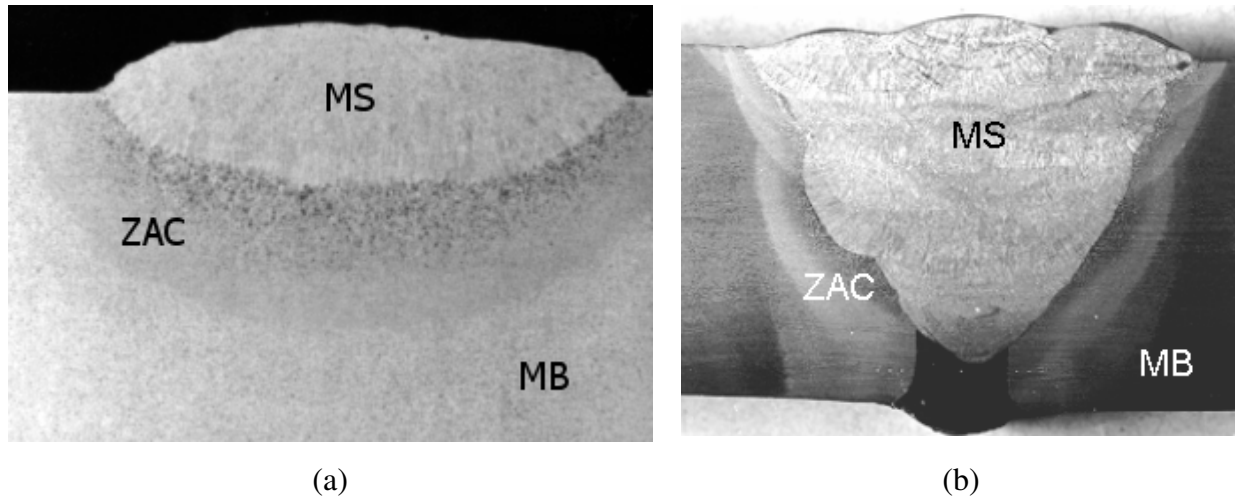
Macrografia de junta soldada: (a) passe único, (b) múltiplos passes. Nital 2%. MS - metal de solda, ZAC - zona afetada pelo calor, MB - metal base. Fonte: Barsanti et al. (2001).
